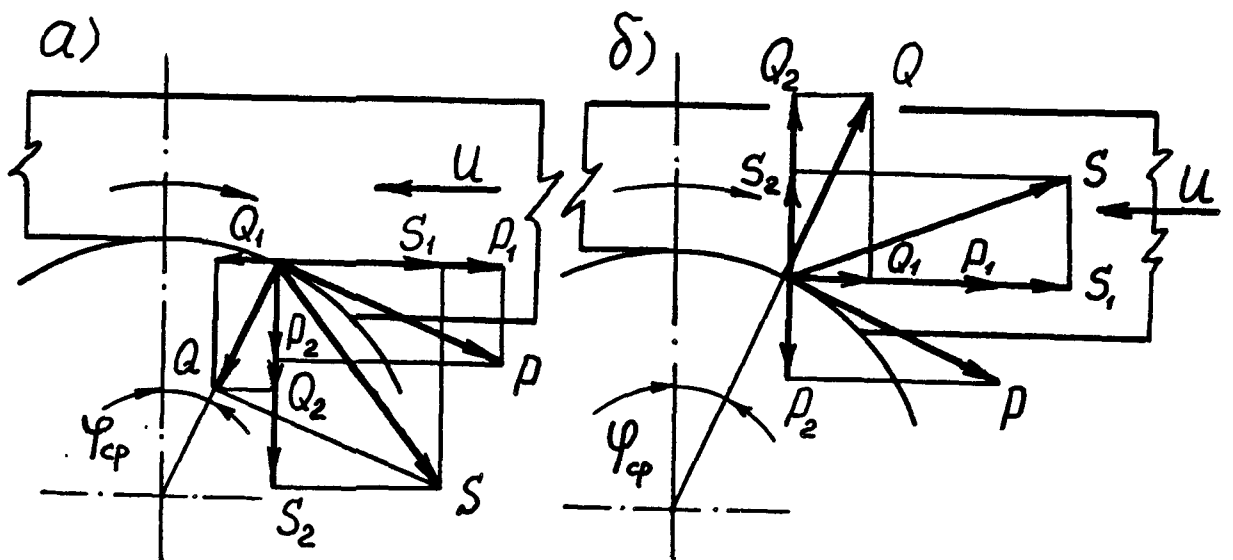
Силы, действующие на заготовку при фрезеровании:
